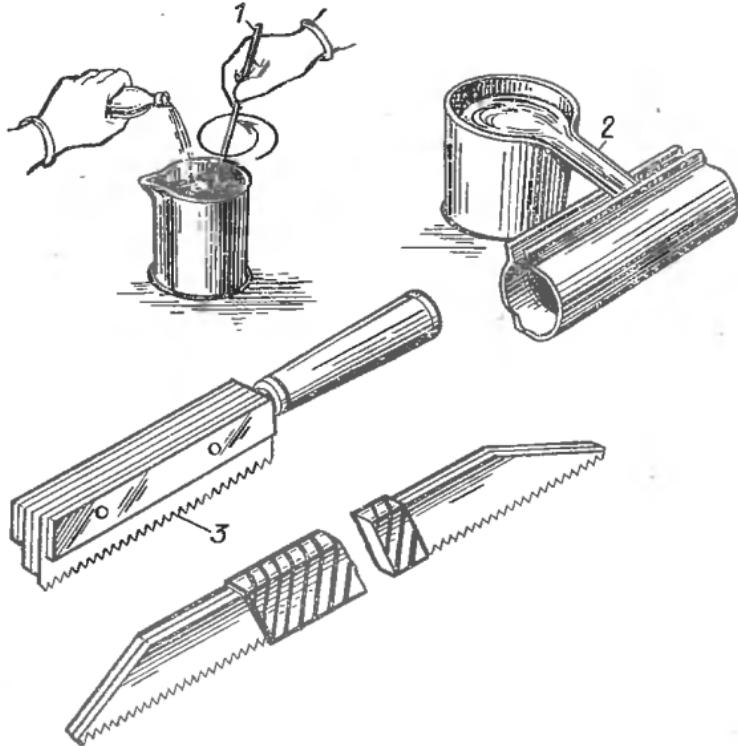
Комплект инструментов и приспособлений для монтажа эпоксидных соединительных муфт:
